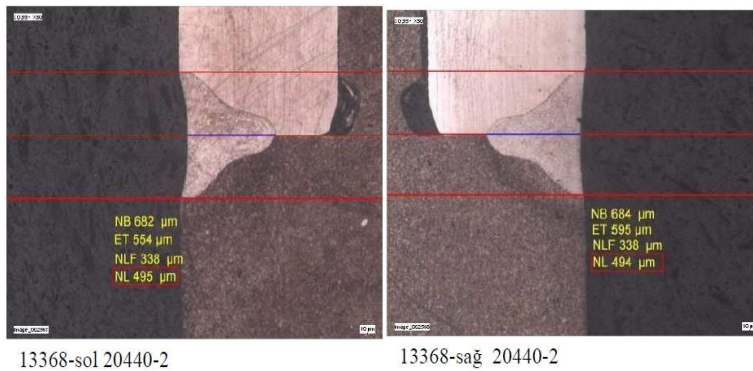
28 0.978 m/dk kaynak hızındaki kaynak dikişi sol ve sağ bölgeleri
